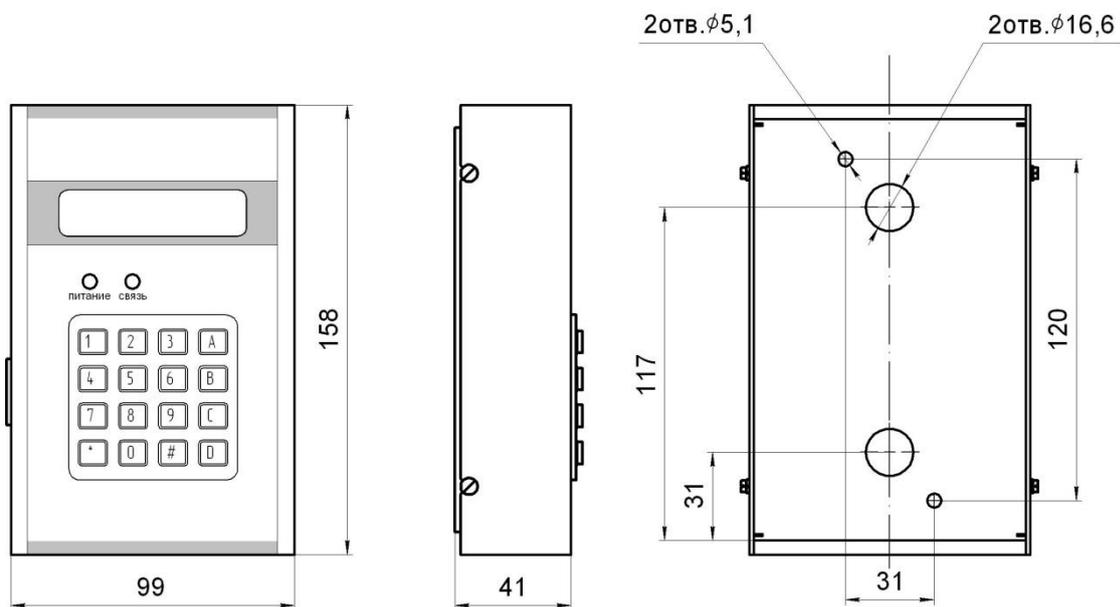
Габаритный чертеж «Зевс-АЛПУ»
